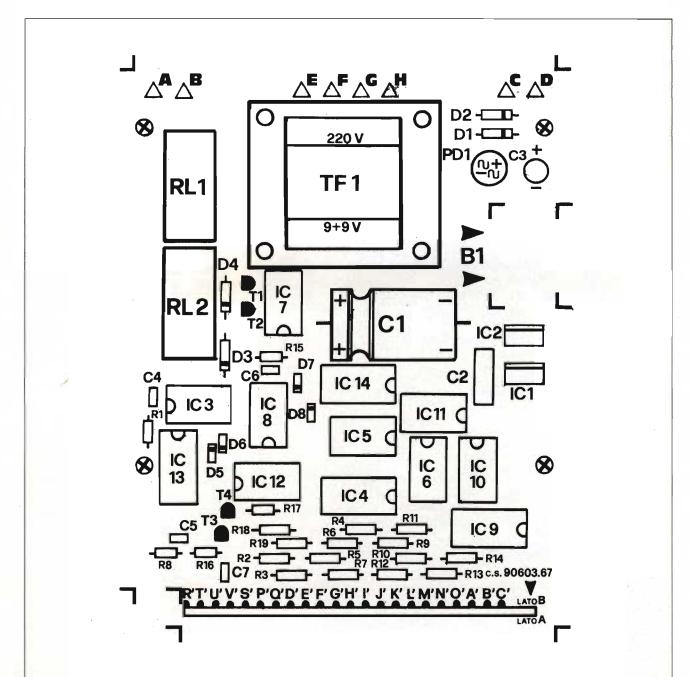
Circuito stampat cod. 90603.66: montaggio dei componenti (lato A).
